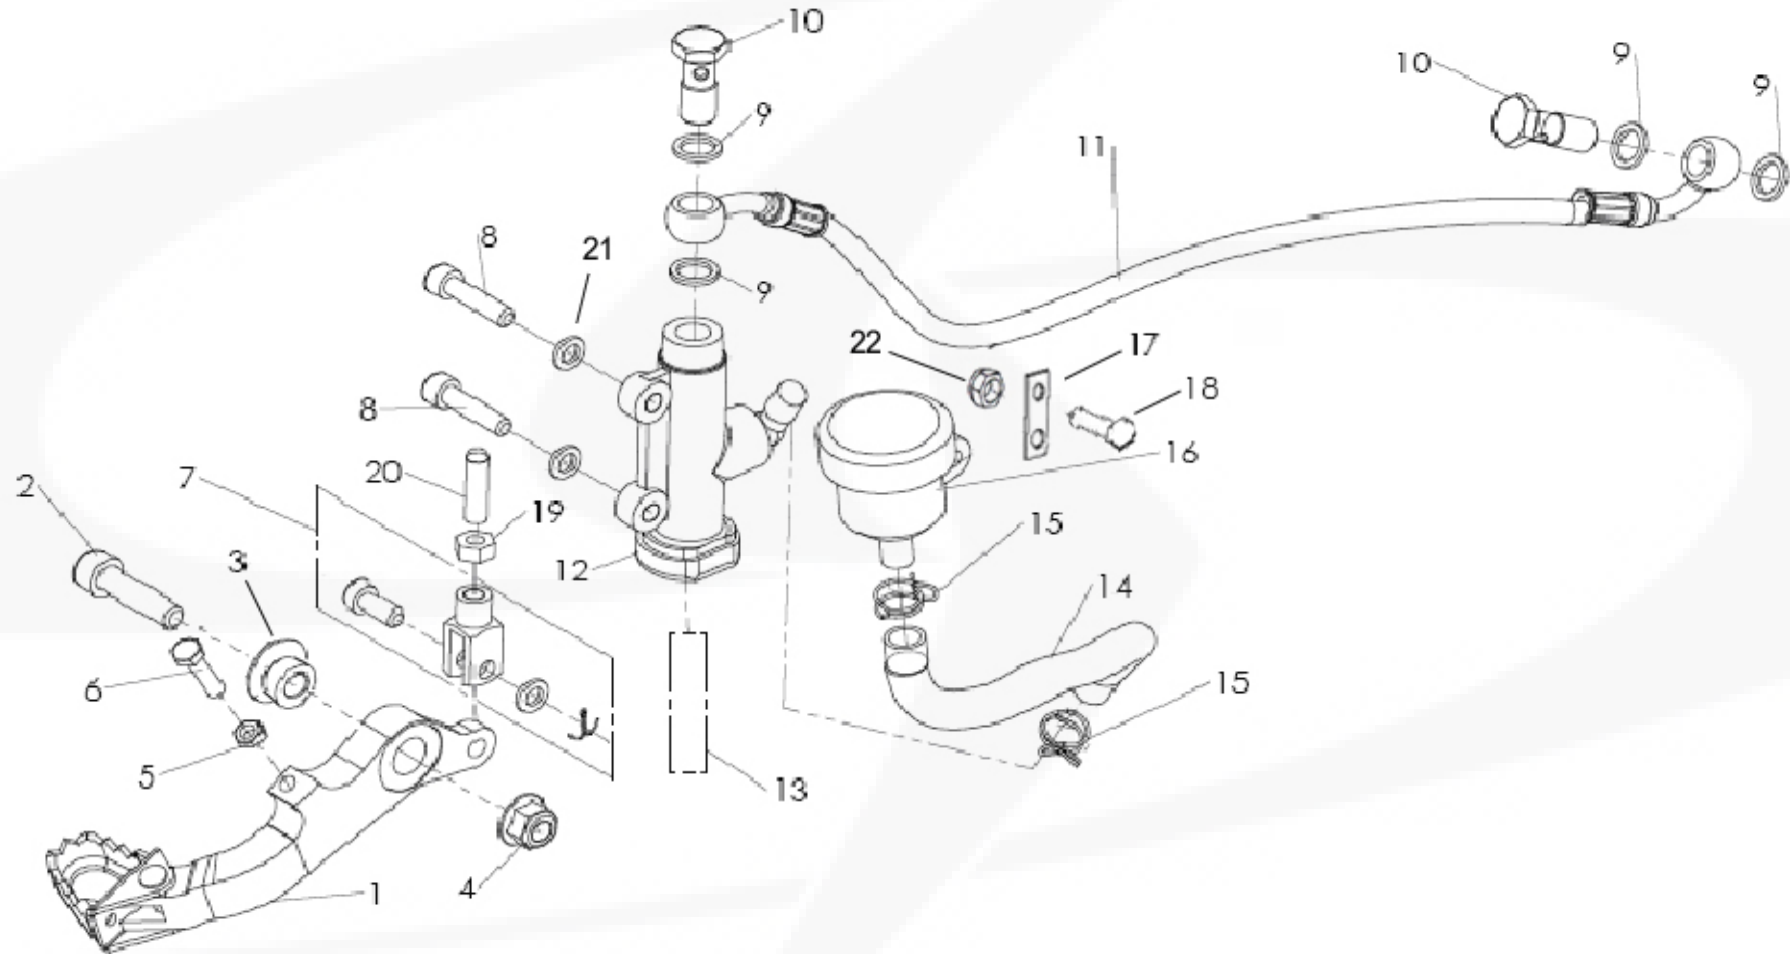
MAÎTRE CYLINDRE FREIN ARRIÈRE / REAR BRAKE MASTER CYLINDER / BOMBA FRENO TRASERO
